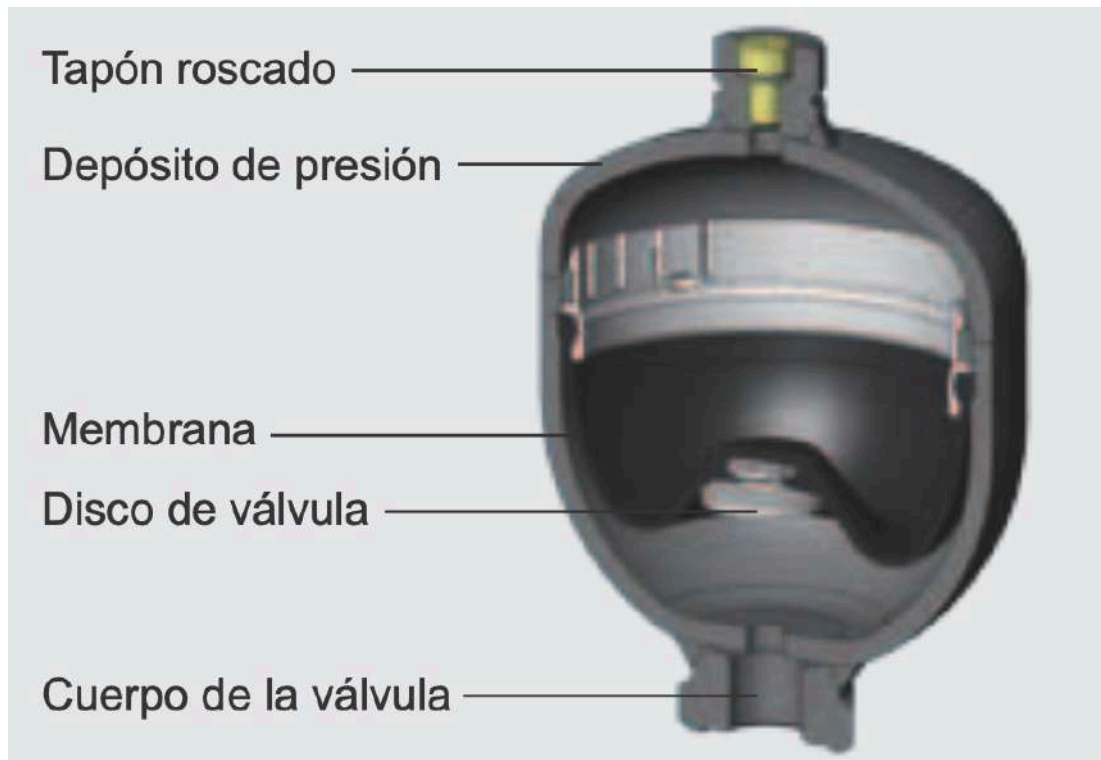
Sección de un acumulador de construcción soldada. Fuente Hydac
